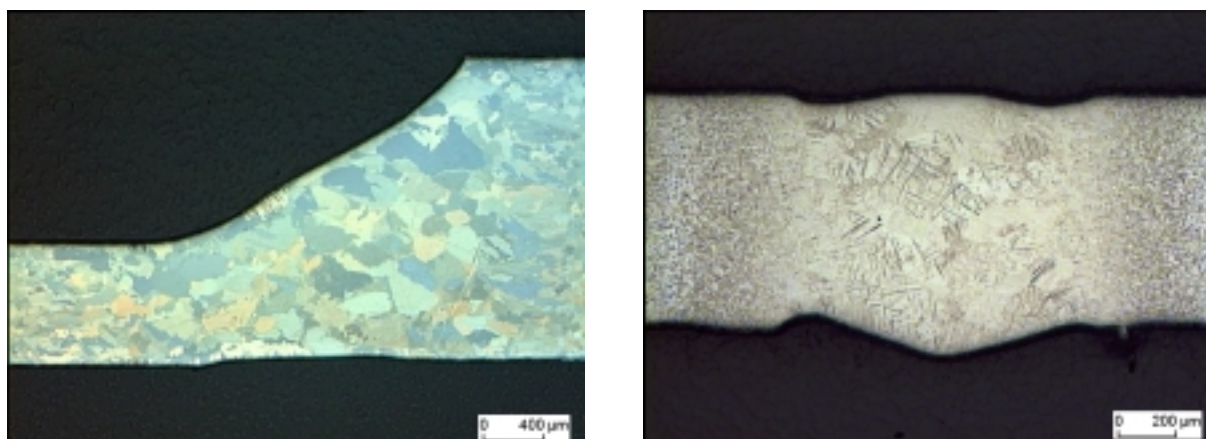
Ti grau 2 (esquerda) e Ti6Al4V (direita) soldado por laser.
